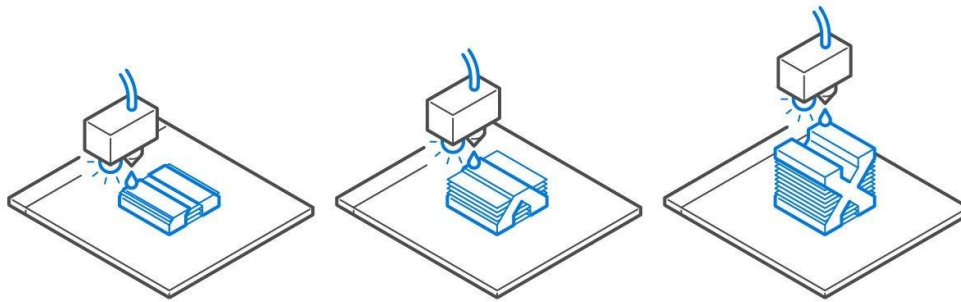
Técnica de impresión 3D por inyección de material. [23]
